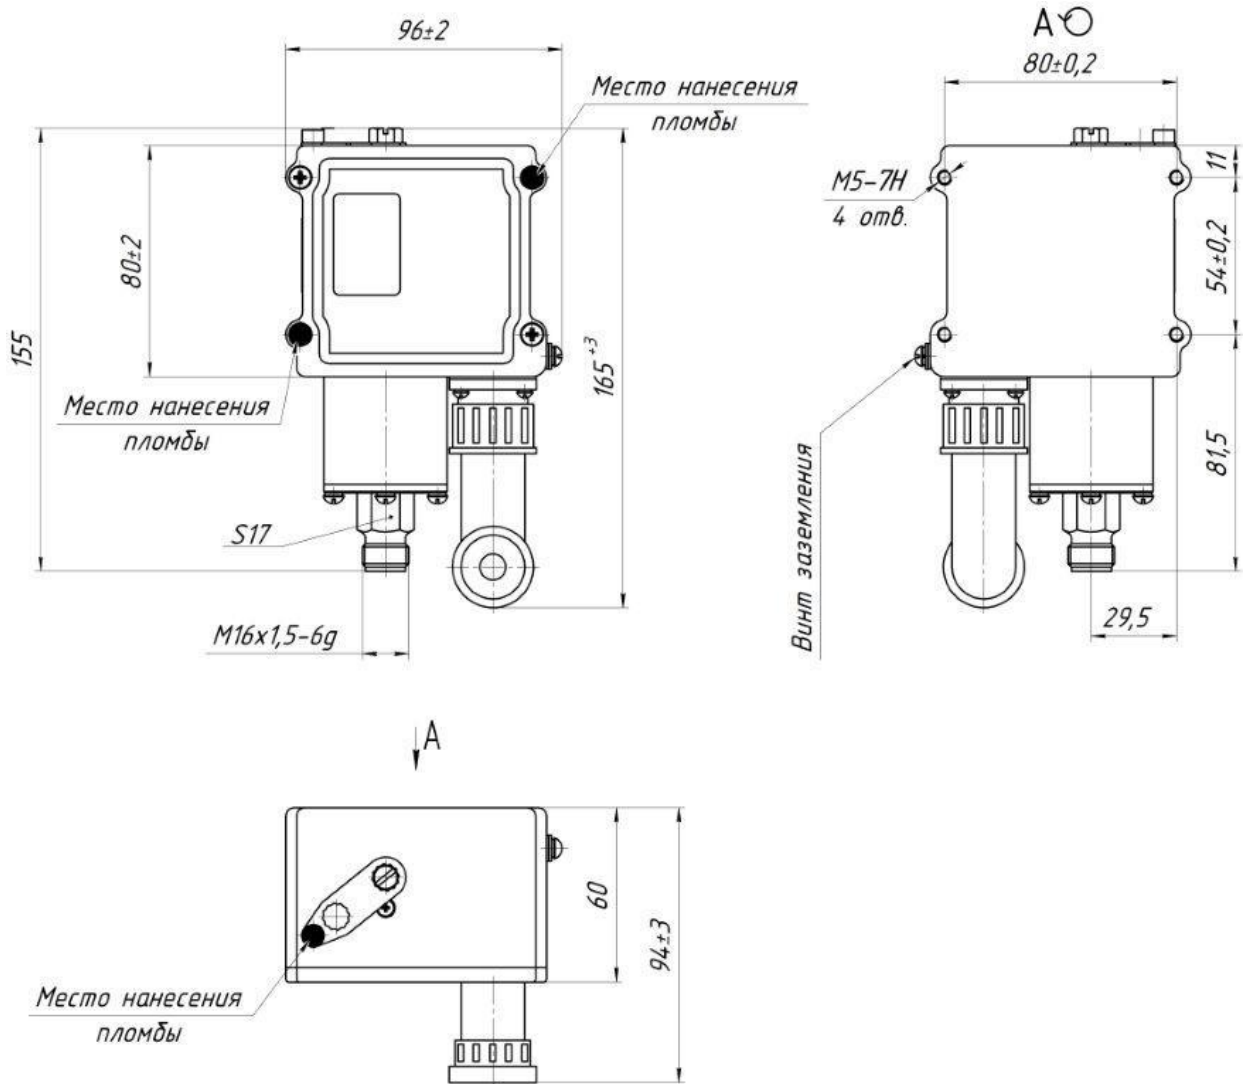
Габаритные и установочные размеры прибора с соединителем типа 2РТТ, ШР с угловым патрубком
